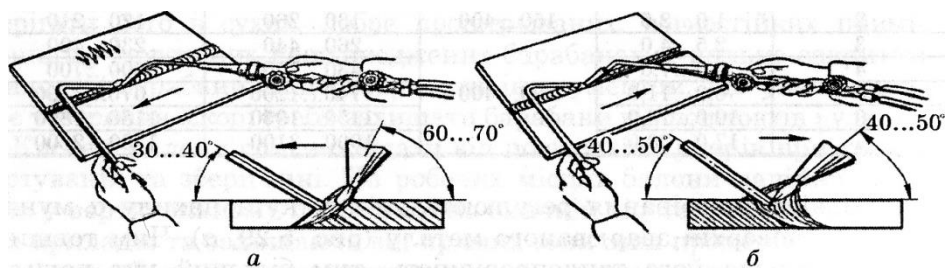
Способи газового зварювання залежно від положення полум'я пальника:
